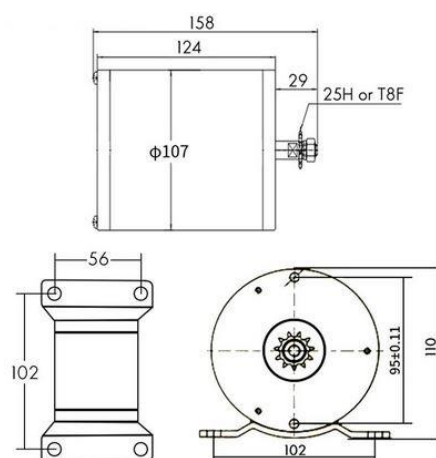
Электродвигатель Kunray и его габаритные размеры
